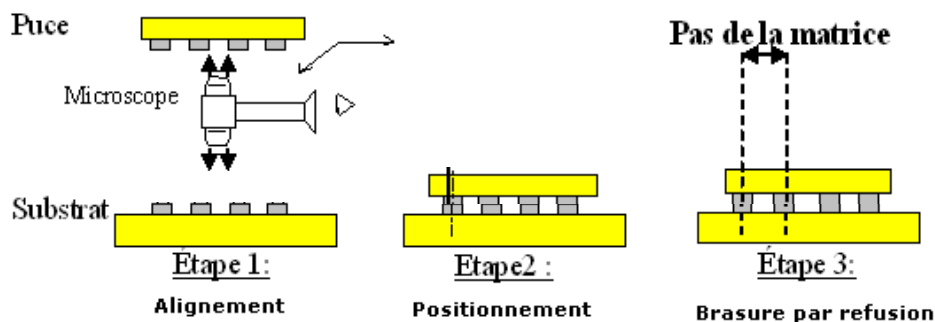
Procédé d'assemblage 'flip-chips' par hybridation
